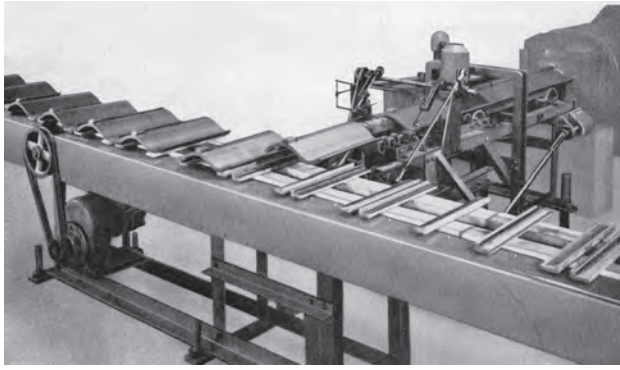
Keller-Vollautomatik für Strangdachziegel mit geschlossenem Kreislauf. Anlage in Betrieb in einem Dachziegelwerk um 1965. Siehe auch Bild 8.128. mit der Grundrißdarstellung der Anlage, bestehend aus Rundbeschicker, Strangpresse, Abscheider, Rollenbahn, Elevator und Niederlaß, jeweils mit Querförderer
